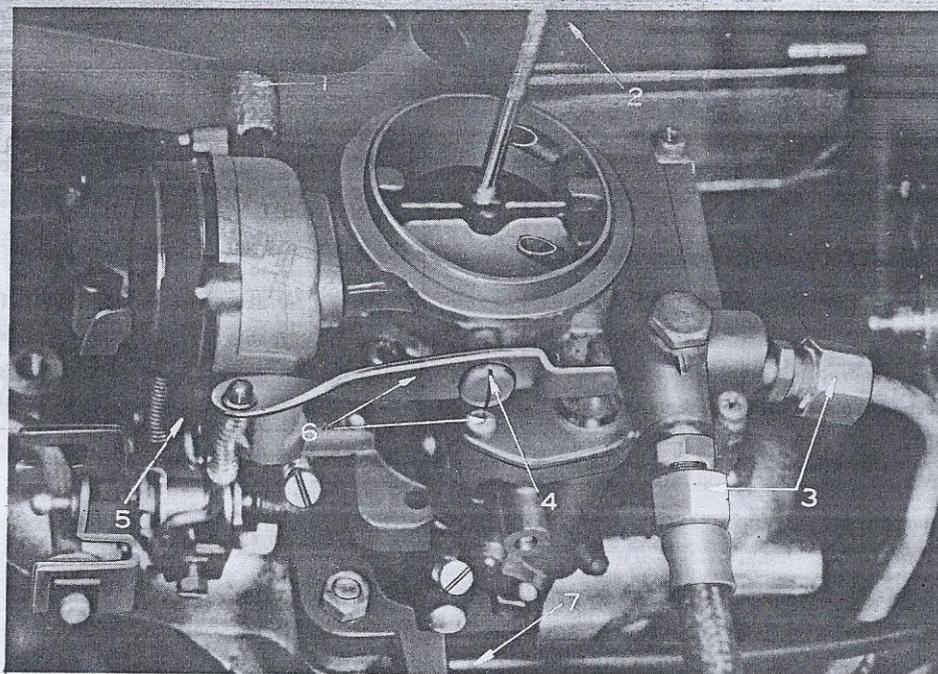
Dépose du dessus de cuve et de l'ensemble du carburateur.
